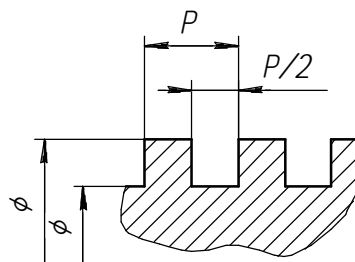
Нанесение размеров прямоугольной и квадратной нестандартной резьбы
